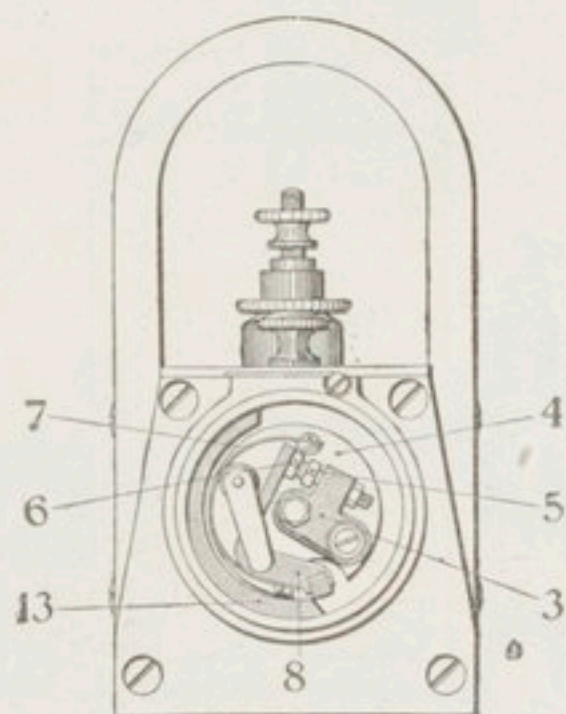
Vue arrière de la magnéto à bougie Bosch pour moteur à un cylindre.
